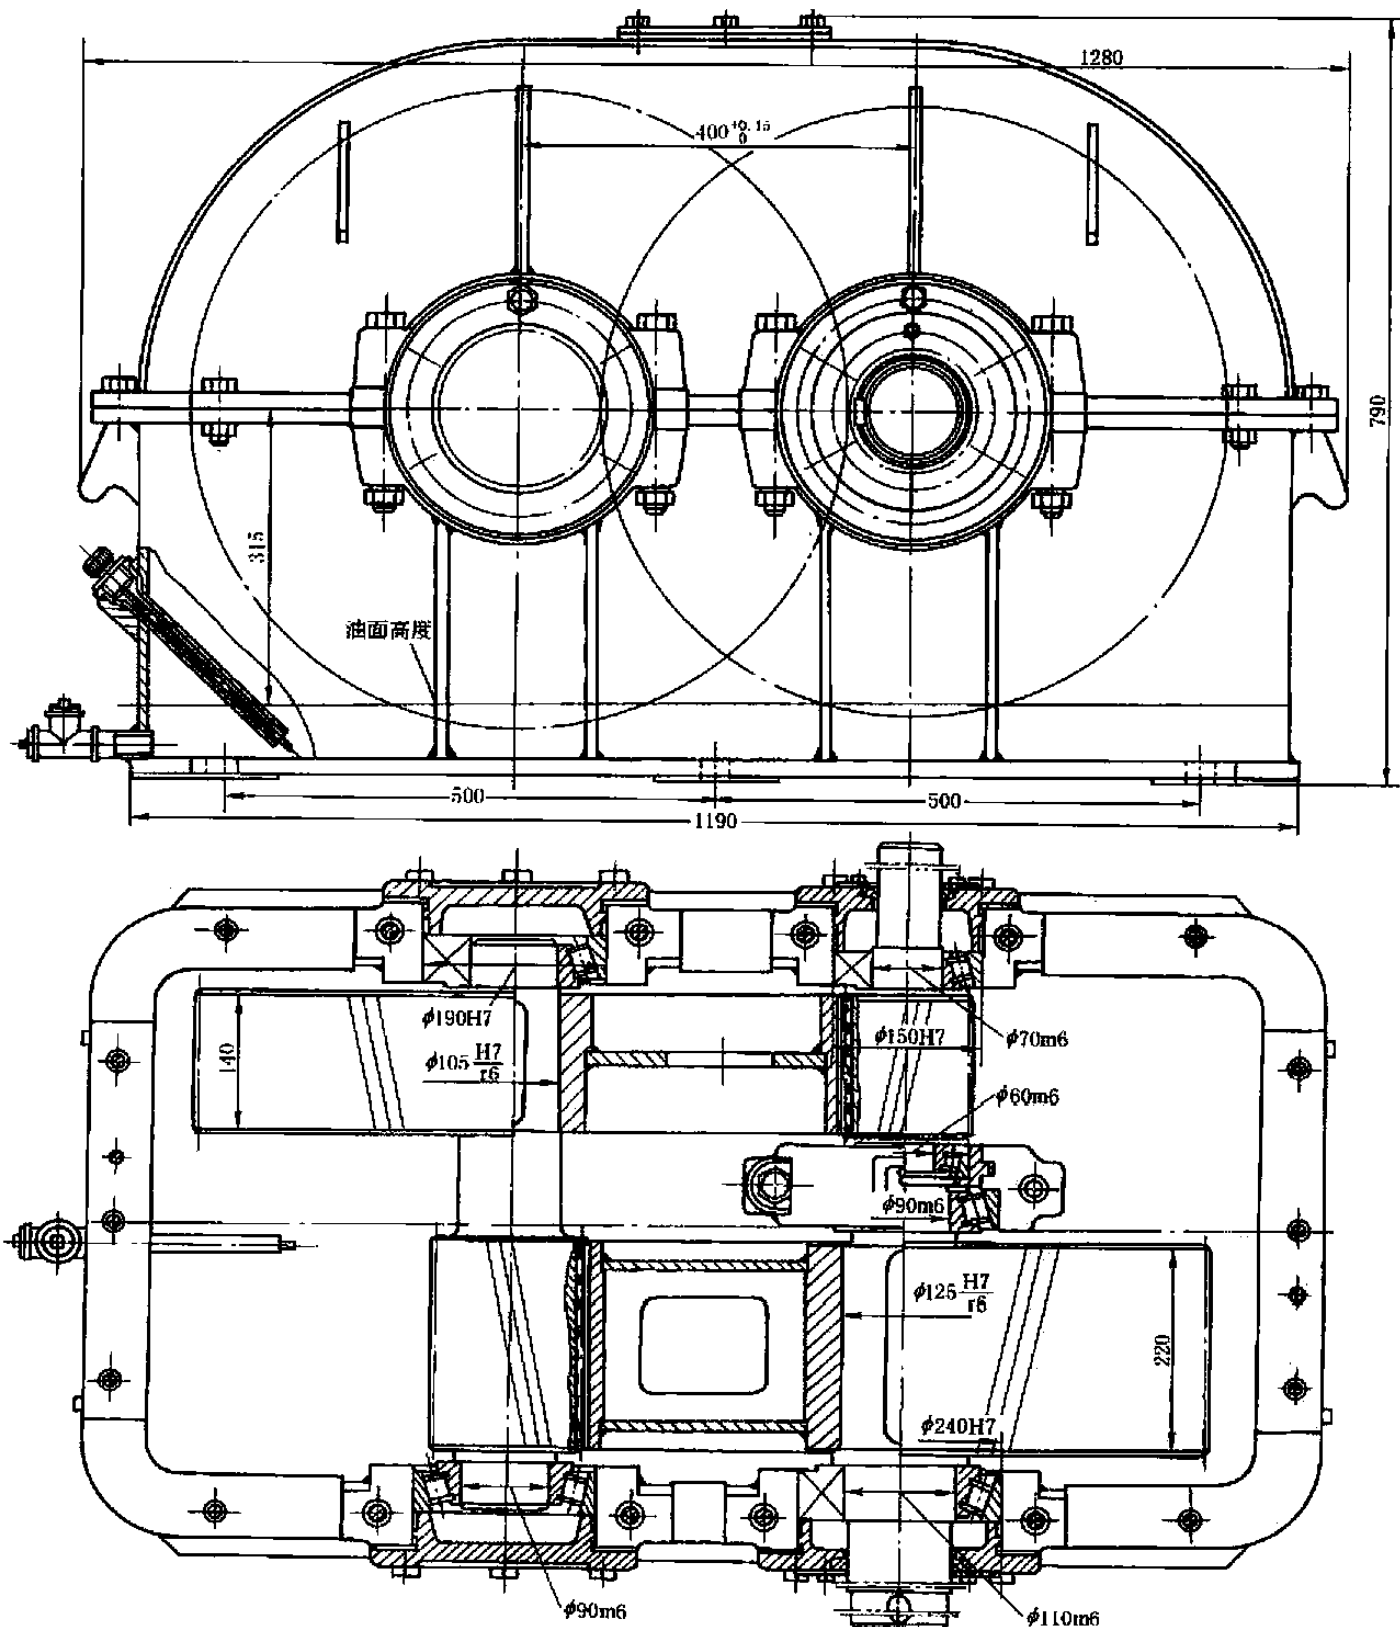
两级同轴式圆柱齿轮减速器 (焊接箱体和大齿轮)
